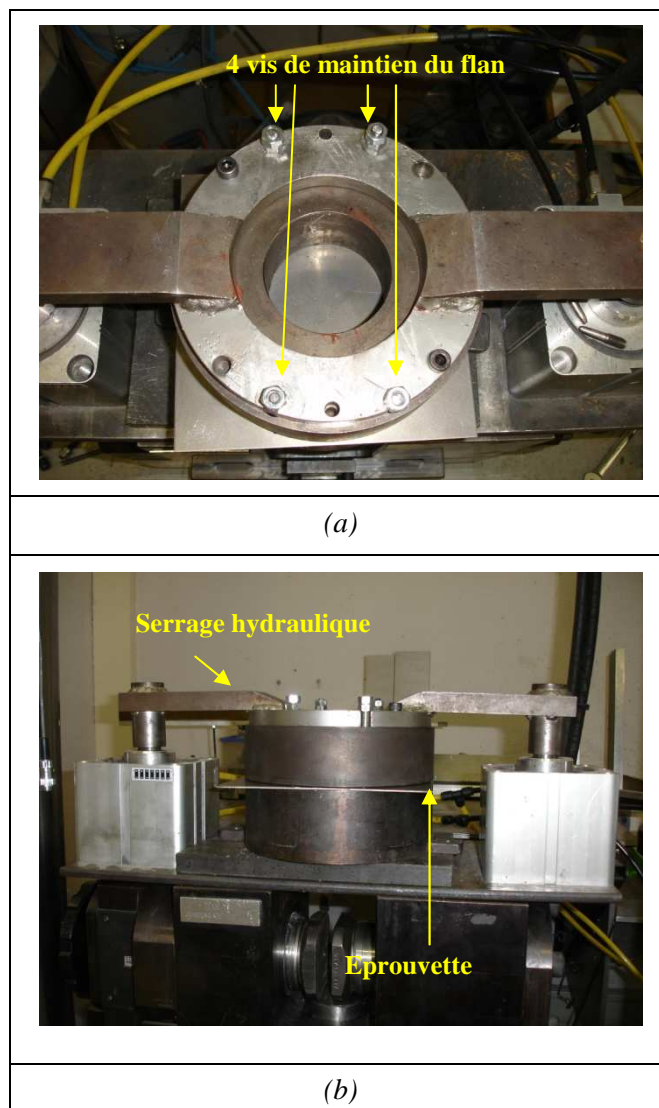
Matrice, serre-flan et éprouvette d'emboutissage installés sur la machine
